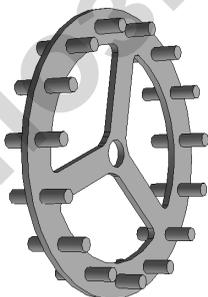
Кольчато-прутковый рабочий орган катковой приставки
